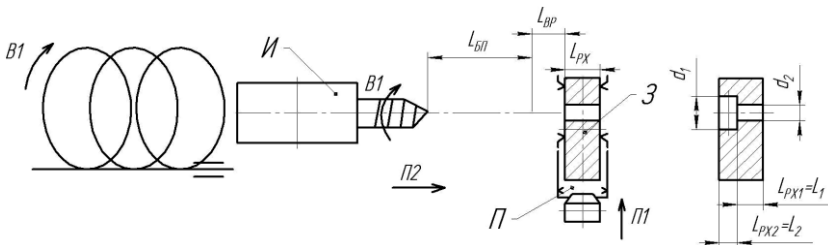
Схема рабочей зоны агрегатно-сверлильного комплекса
